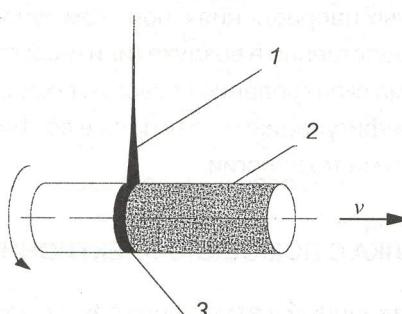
Схема закалки электронным пучком цилиндрических деталей: 1 – рассеивающийся в воздухе электронный пучок; 2 – закаленный слой; 3 – кольцо разогрева
